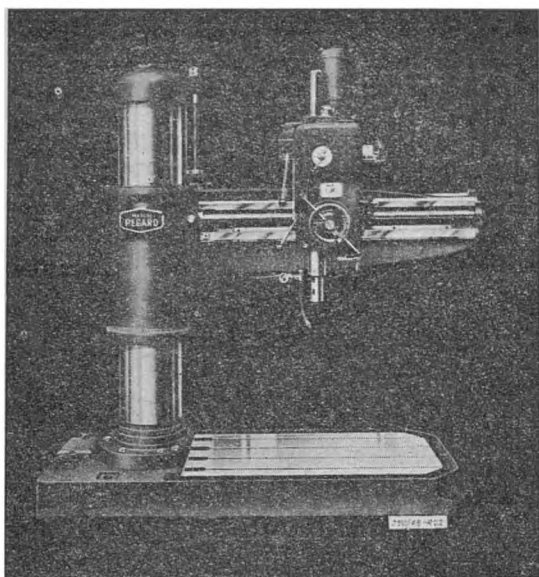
Wiertarko-frezarka Pegard typ 924, średnica wrzeciona 80 mm, średnica wytaczania 800, 18 prędkości wrzeciona od 10 — 1600 obr/min, moc 7—8 KM, ciężar 6600 kG.
